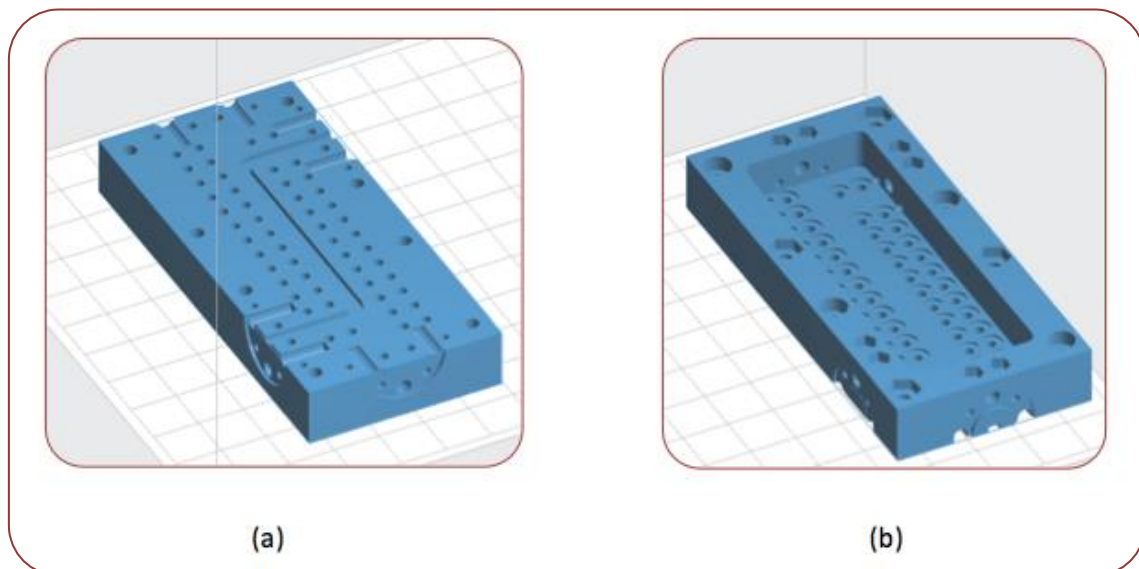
(a) Diseño 3D de acoplador mitad inferior ;(b) Diseño 3D de acoplador mitad superior.
